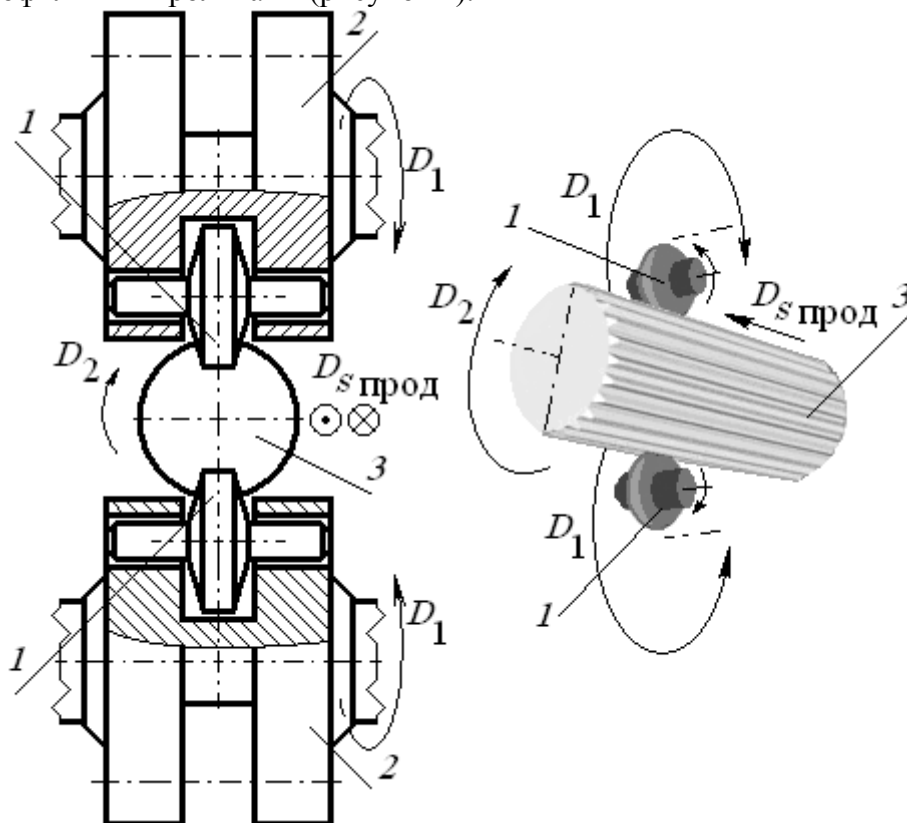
Схема накатывания мелко модульных зубчатых венцов двумя профильными роликами: 1 – ролик; 2 – накатная головка; 3 – заготовка; D_1 , D_2 – вращательные движения соответственно оправки и заготовки; $D_{s \text{ прод}}$ – продольное движения подачи.
